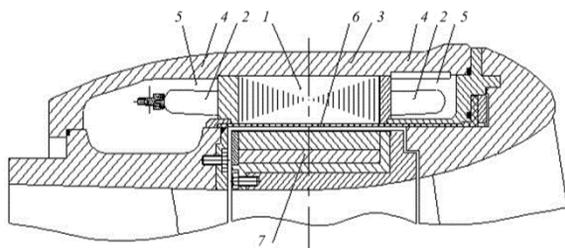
Электродвигатель: 1 – сердечник статора; 2 – лобовые части обмотки ротора; 3 – корпус над сердечником статора; 4 – корпус над лобовыми частями обмотки статора; 5 – трансформаторное масло; 6 – изоляционная гильза статора; 7 – ротор с постоянными магнитами
